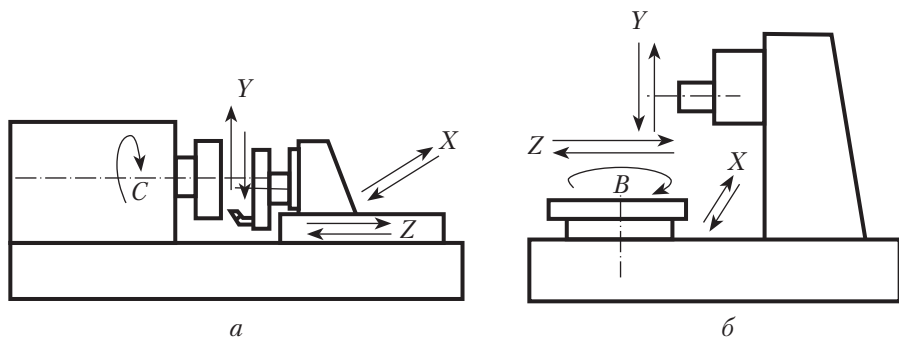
Токарный патронный (а) и горизонтально-расточной (б) станки с ЧПУ
